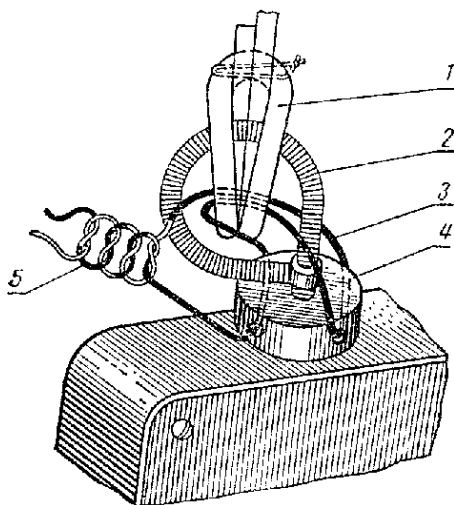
Контровка гибкой шпильки прибора ППК-У:
